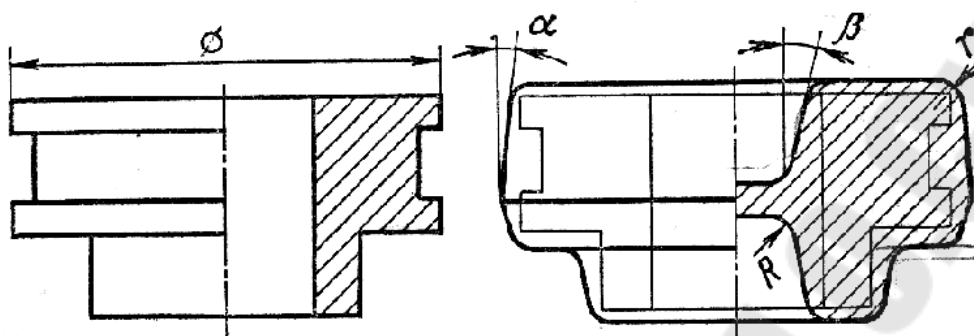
Чертеж поковки, получаемой штамповкой
